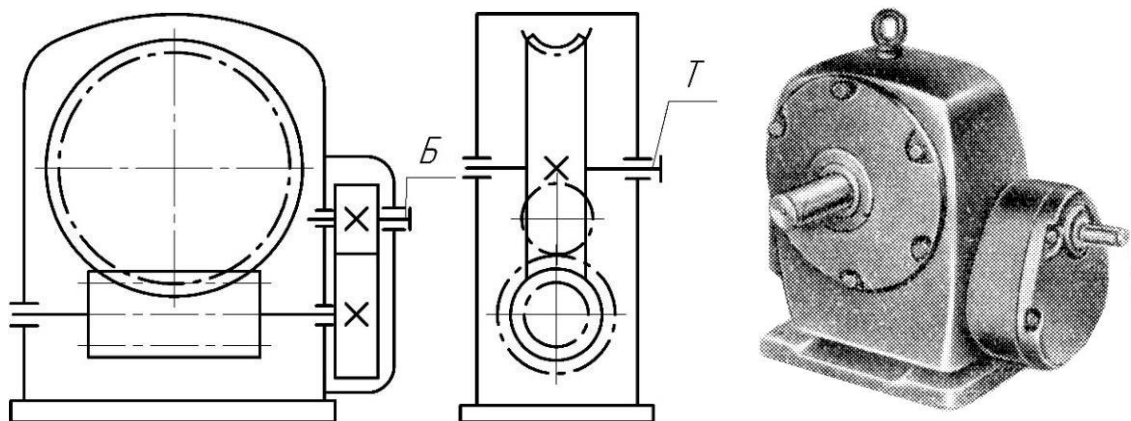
Двухступенчатый зубчато-червячный редуктор
